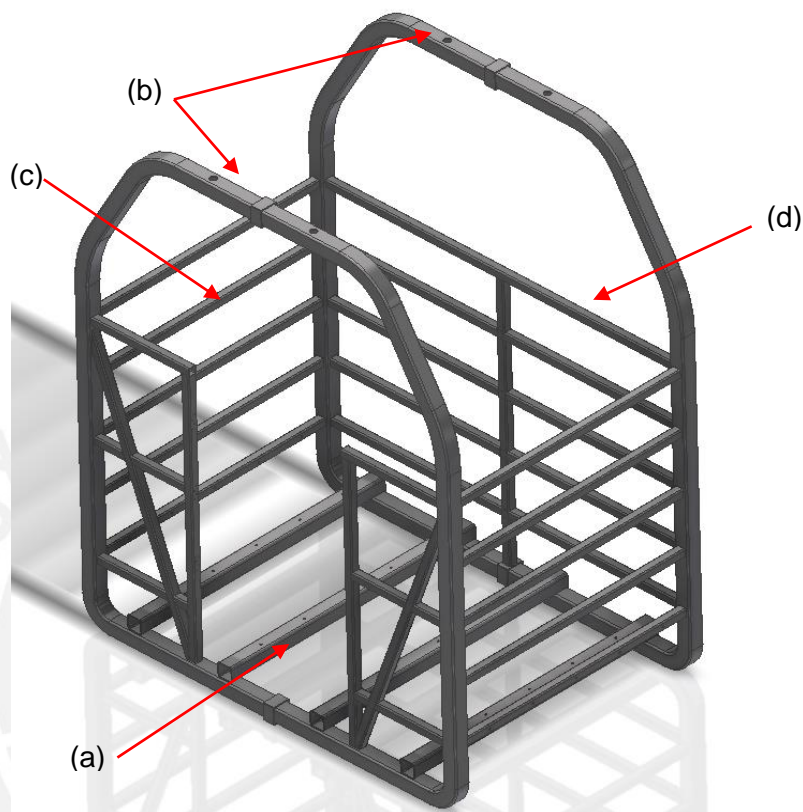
Estructura de la canasta: Perfiles transversales para el piso (a), arcos de soporte (b), perfiles transversales laterales (c), perfiles rigidizadores (d). Fuente: Elaboración propia.
